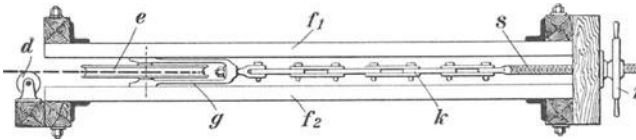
Spannschlitten mit Laschenkette und Schraubenspindel.
